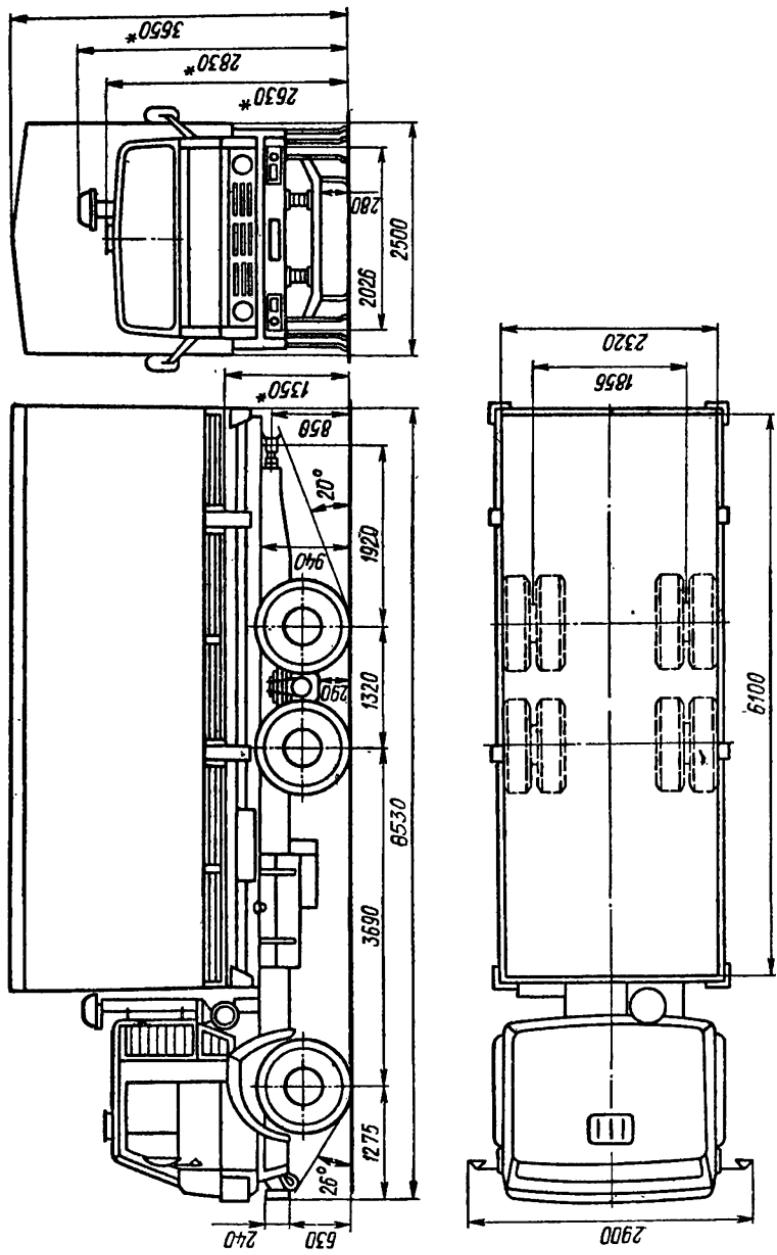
Габаритные размеры автомобиля КамАЗ-53212
